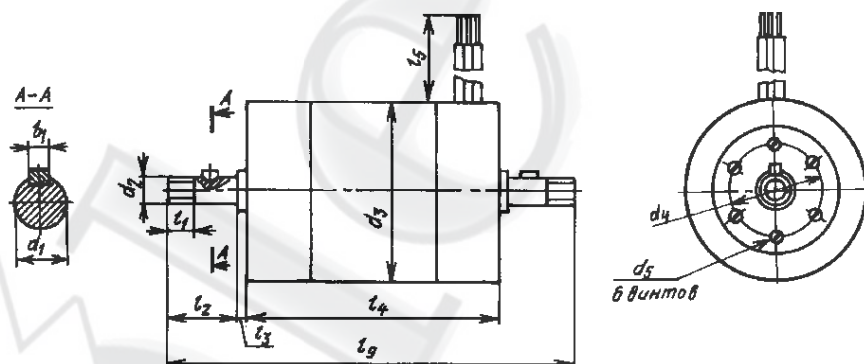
Габаритные и присоединительные размеры двигателей (исполнение с креплением на хомутах с двумя свободными концами вала)
